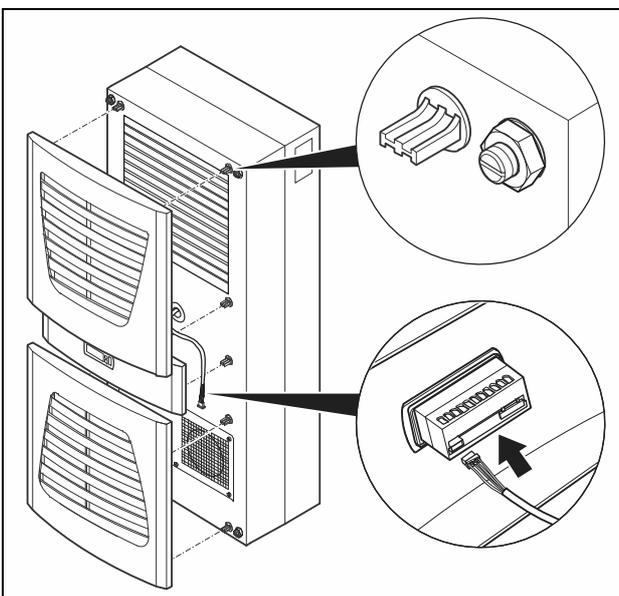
Brancher l'afficheur et mettre la grille à lamelles en place
